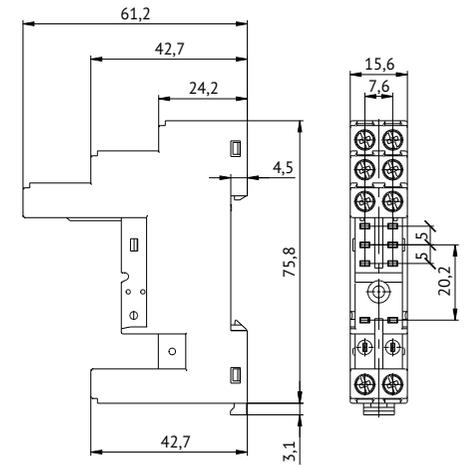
Габаритные, установочные и присоединительные размеры розетки OptiRel G RR95-02
